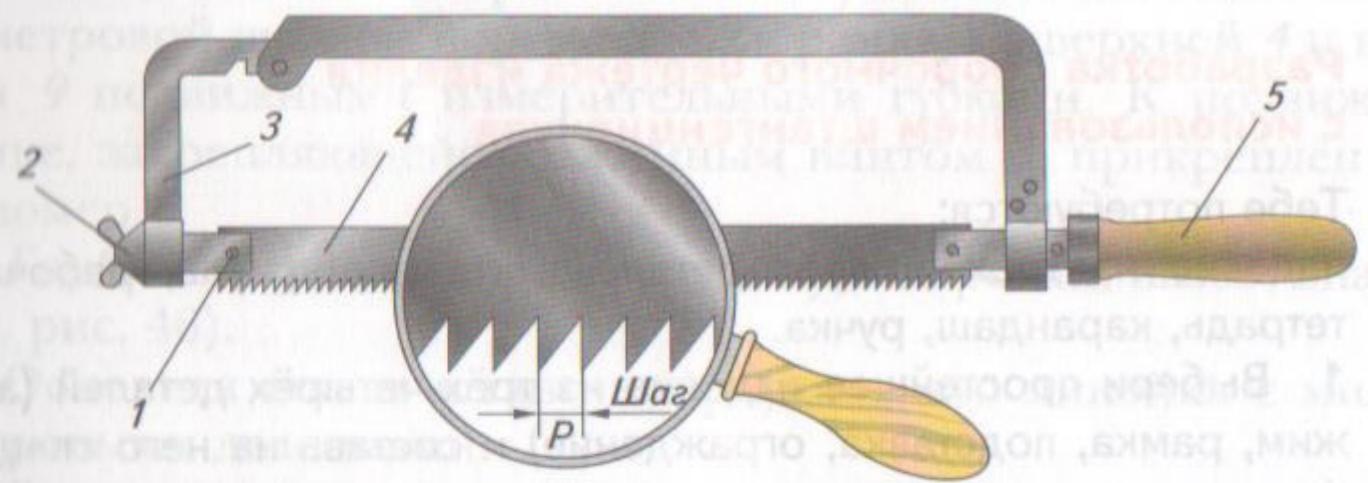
Устройство слесарной ножовки: 1 — штифт крепления полотна; 2 — натяжная гайка; 3 — рамка; 4 — ножовочное полотно; 5 — ручка
